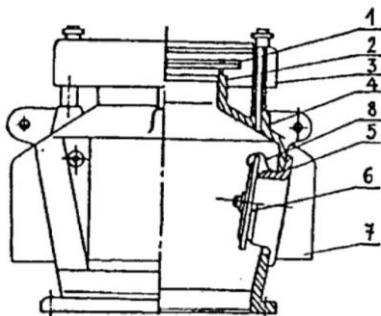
Клапан тип КДС: 1 – тарелка давления; 2 – седло давления; 3 – крышка; 4 – корпус; 5 – седло вакуума; 6 – тарелка вакуума; 7 – кожух; 8- гибкая фторопластовая пластина
